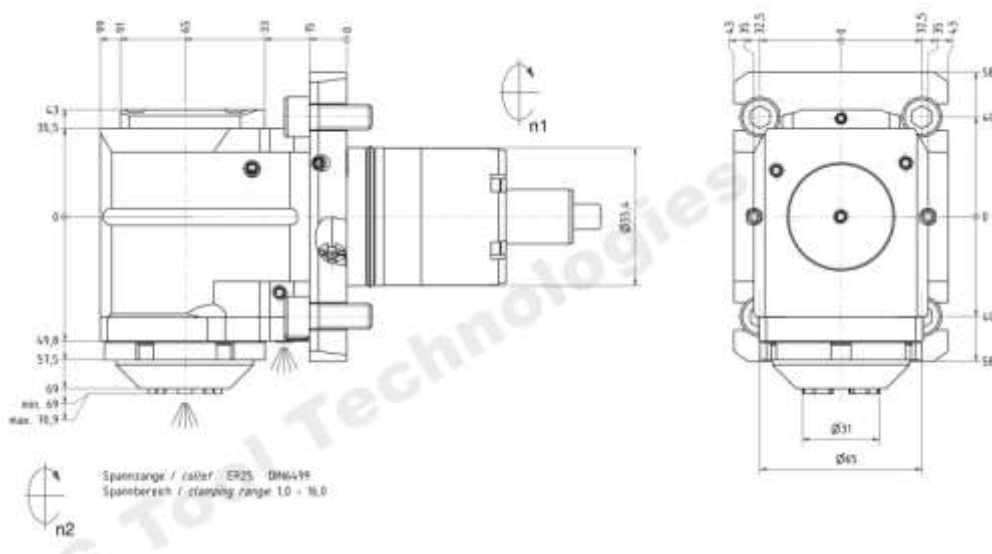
Сверлильно-фрезерная головка 60.55.425LT2000V16IKGLIM
